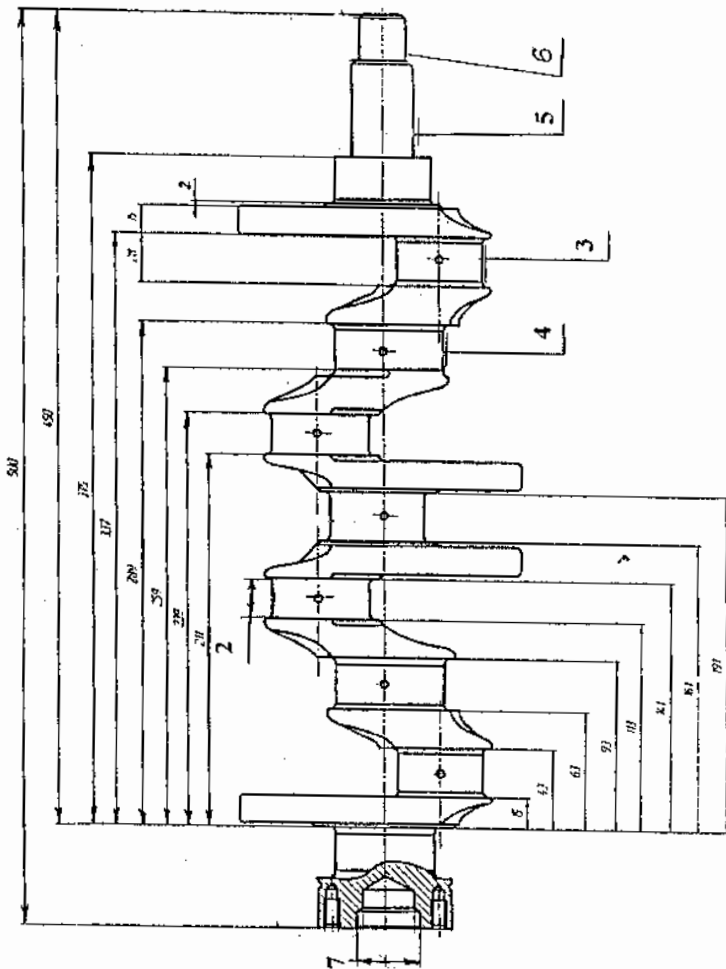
Коленчатый вал двигателя ВА3. Материал: Чугун ВЧ 50-2
